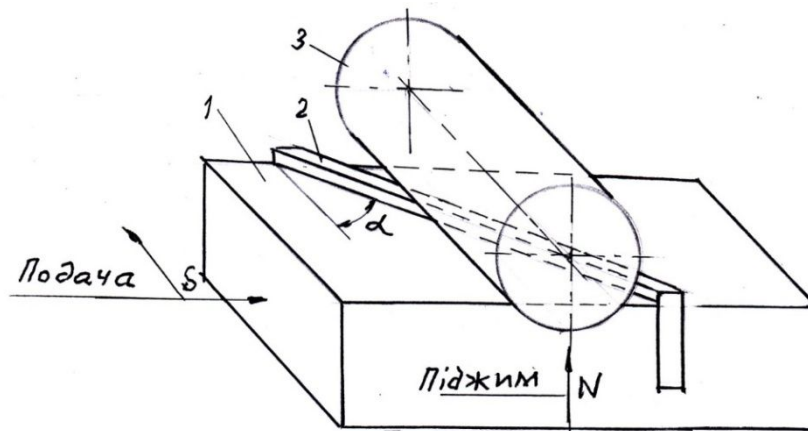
Схема контакту латунної пластинки з валом, що обробляється за допомогою пристосування для фрикційного латунювання з наклонним інструментом: 1 – касета; 2 – латунна пластинка; 3 – деталь
